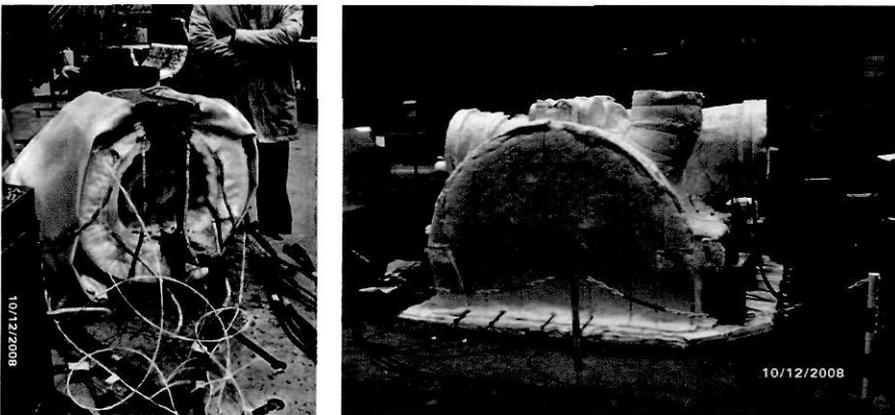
Schweiß-Arbeitsprobe im Originalmaßstab und Glühung des Gehäuses nach erfolgter Reparaturschweißung.
